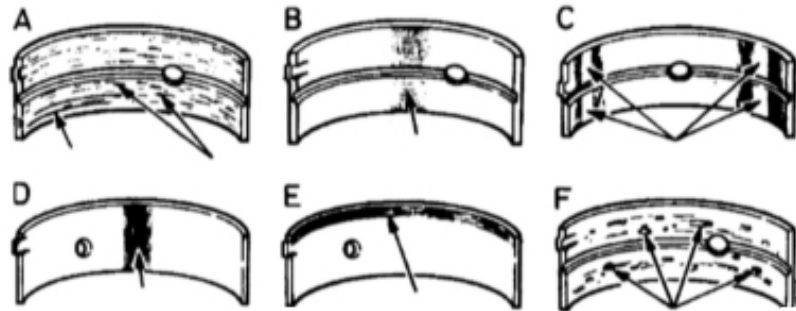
Примеры износа вкладышей подшипников коленчатого вала: А – поцарапаны инородными частицами – видны крупницы, погружившиеся в рабочий слой вкладыша; В – недостаток масла – верхний слой стерт; С – вкладыши неправильно расположены при установке – имеются блестящие (отполированные) участки; D – шейка сведена на конус – верхний слой снят со всей поверхности; E – износ края вкладыша; F – неисправность “усталости” – образовались кратеры или карманы [2]
